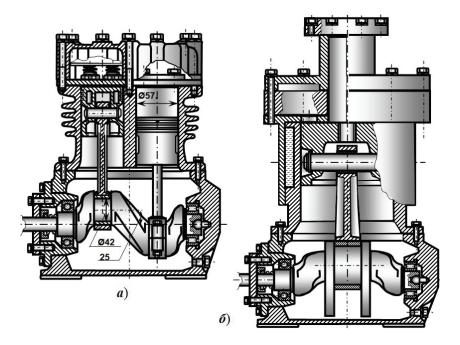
Двухцилиндровый одноступенчатый компрессор Ф-6 (a) и его модернизация до поршневой ГМОД (б)
